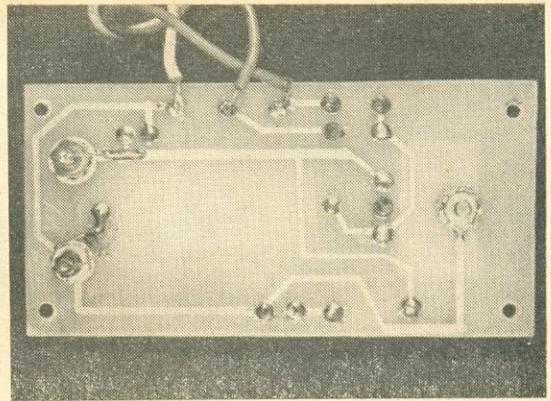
FOTO II — Plaqueta da fonte, completamente montada e pronta para a utilização. O único componente externo à plaqueta foi o transformador T1 que, devido a seu peso e dimensões, deverá ser fixado à caixa que alojar os módulos do LAB Digital.
